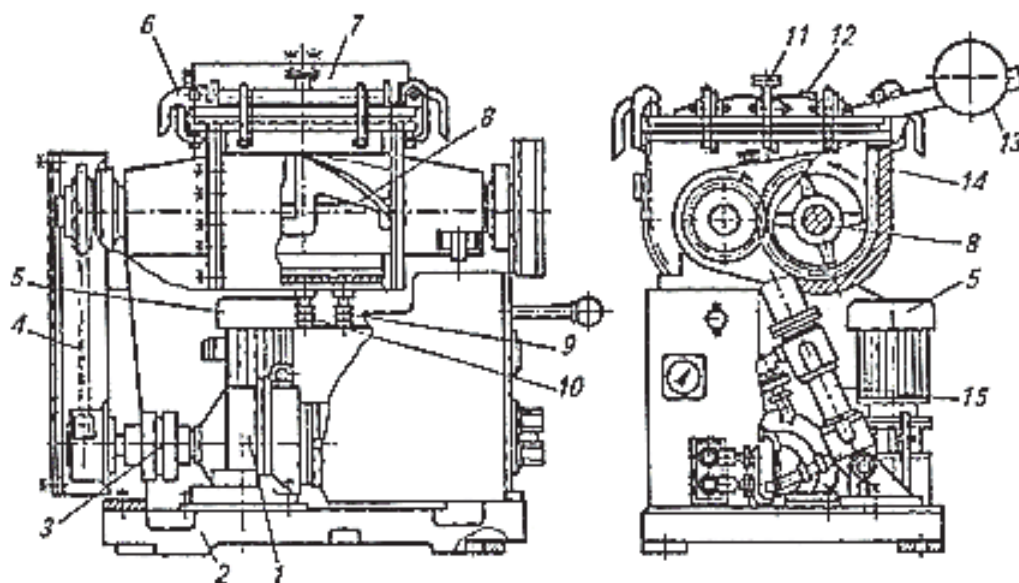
Двухроторный смеситель с Z-образными лопастями
